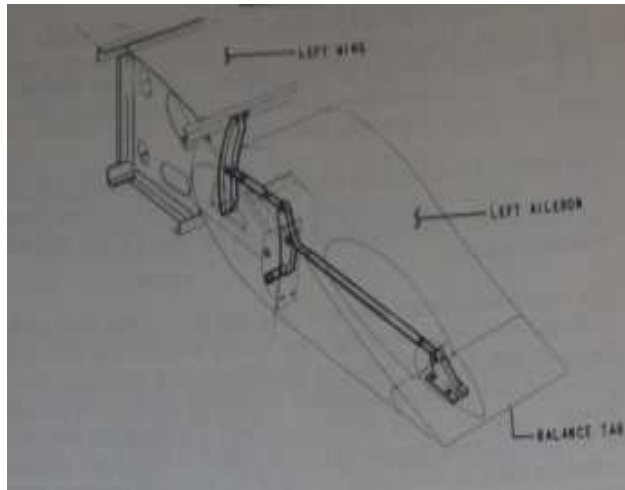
Mecanismo Actuador del Balance Tab en el ala izquierda
